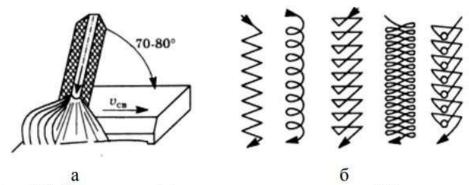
Положение (a) и поперечное движение (б) электрода при сварке нижних стыковых швов
